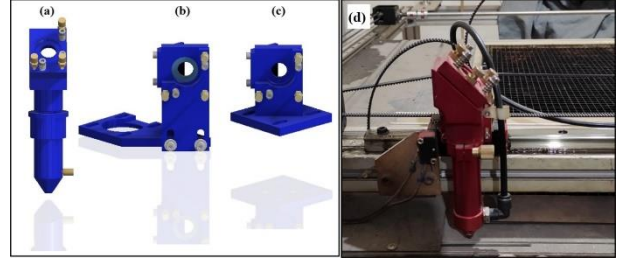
Hareket sistemi ve parçalarının makine üzerindeki durumu (Demonstration of the travel system and its parts on the machine)
